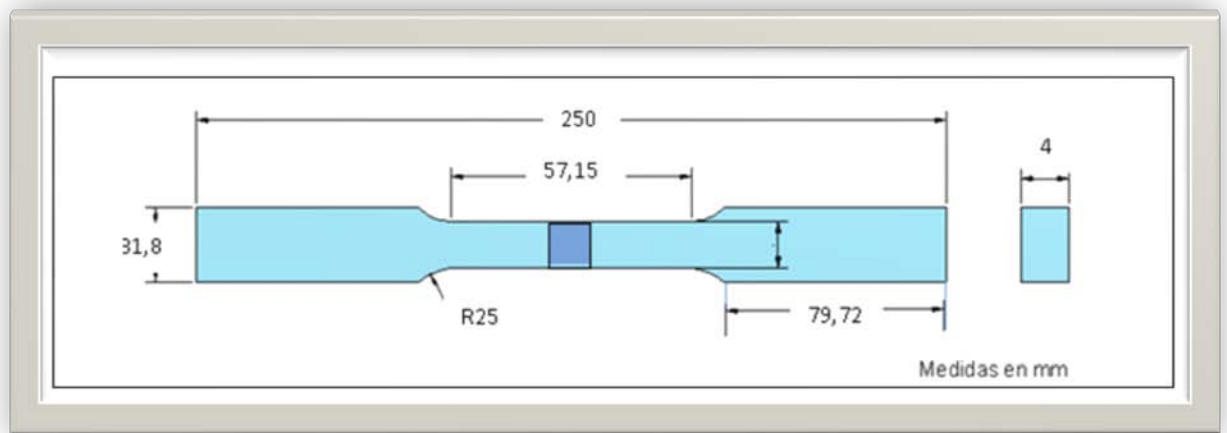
Probeta de tracción de la soldadura
